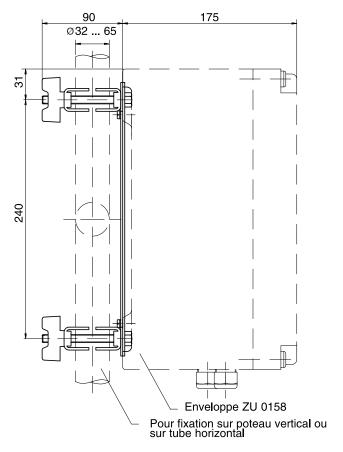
Jeu de colliers pour fixation sur mât ZU 0220 pour boîtier de protection ZU 0158
